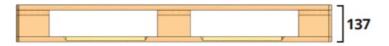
Esquema de vista lateral de um pallet com 137 mm de altura
